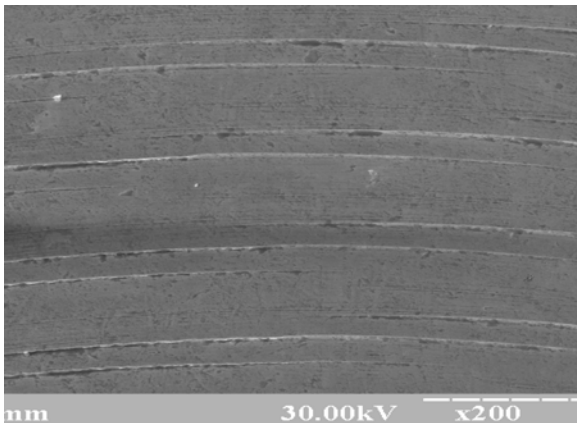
Образцы поверхностей, обработанных фрезами с различными радиусами режущих кромок
